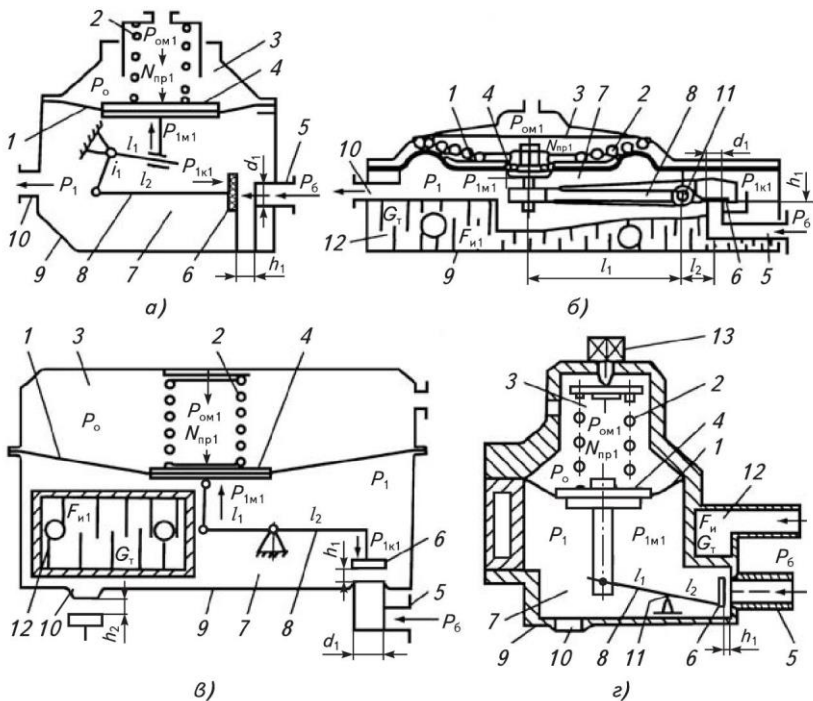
Розрахункова принципова схема першої ступені газового редуктора з системою важільної передачі зусиль
